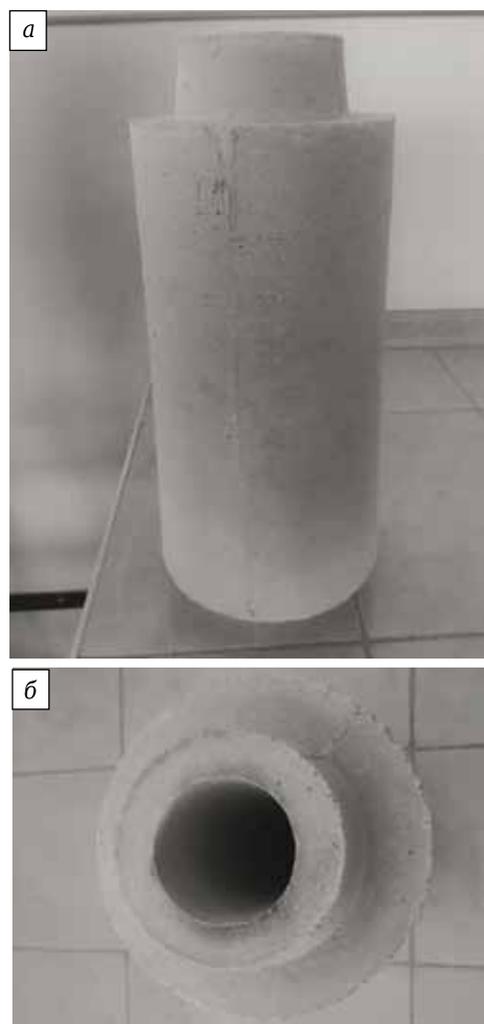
Общий (а) и внешний вид стакана-дозатора (б)
